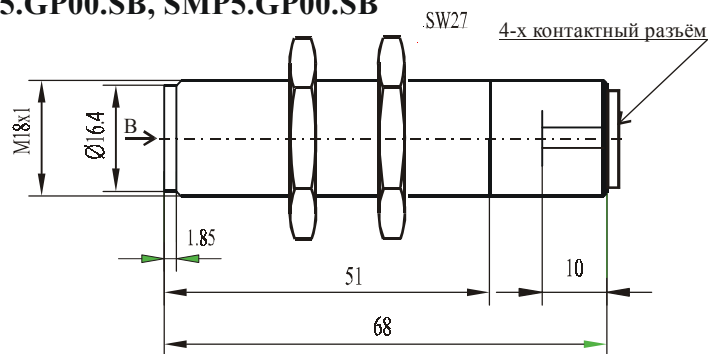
Внешний вид и габаритные размеры датчиков типа SMN5.GP00.SB и SMP5.GP00.SB
